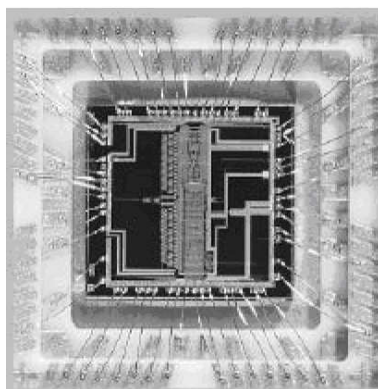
Interconnexions réalisées par soudage par fil
